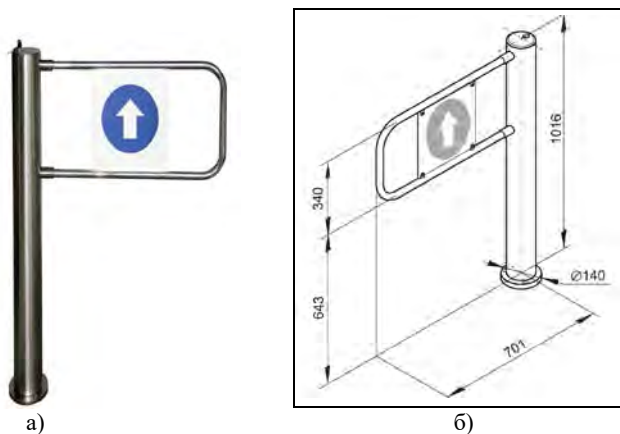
Калитка электромеханическая: внешний вид, габаритные размеры
